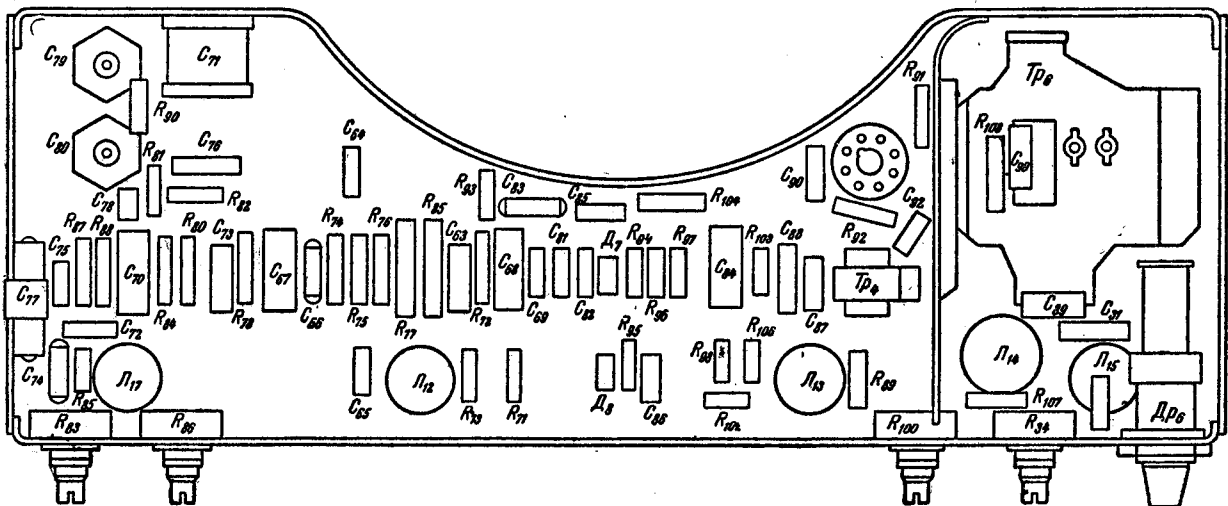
Расположение деталей на шасси блока разверток (вид со стороны монтажа).
